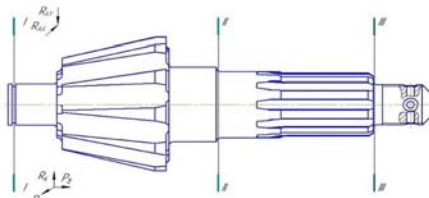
Ведущий вал мотор-редуктора сепаратора ПБС-90/210 и схема его нагружения
